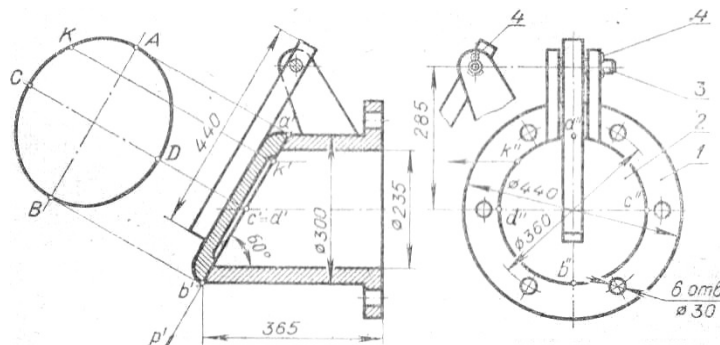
Хлопушка резервуарная: 1-корпус, 2-крышка с рычагом, 3-ось, 4-шплинт
